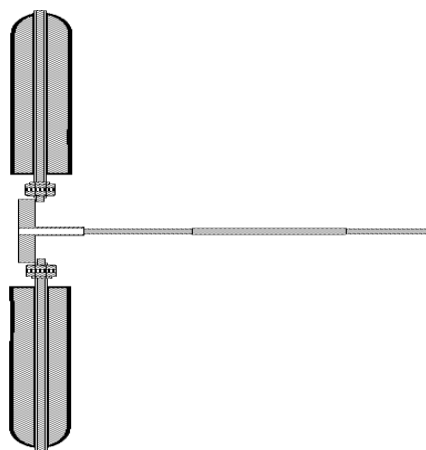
Основная ось и вращающиеся цилиндры заданного сечения макетного образца ветродвигателя (вид сбоку)
